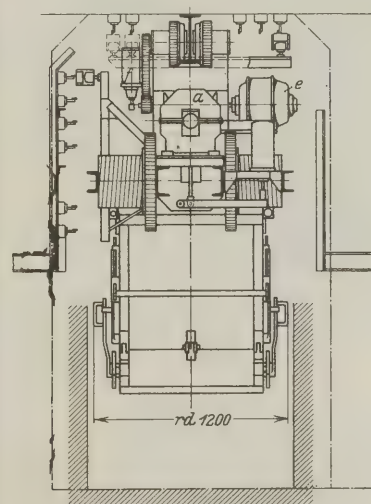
bis 8. Unterflansch-Laufkatze zum Beschicken von Kuppelöfen.
